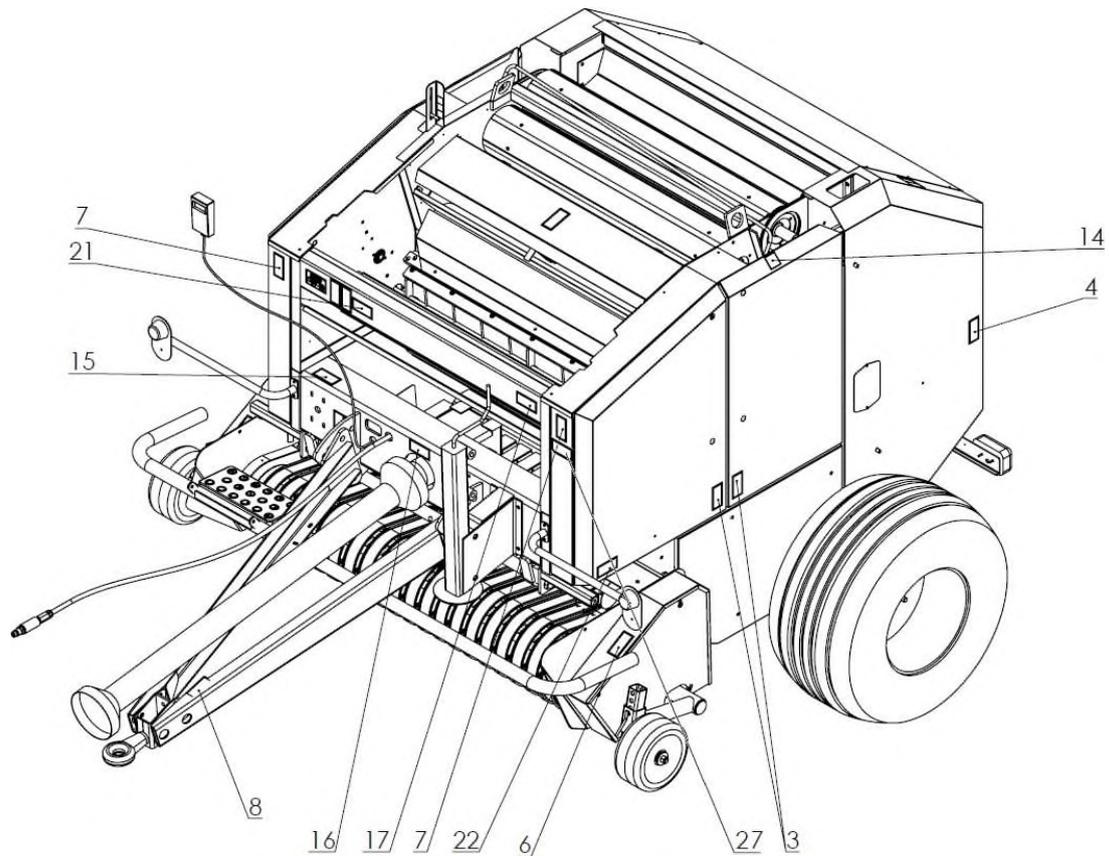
Disposición de los símbolos de seguridad en la máquina - lado izquierdo
